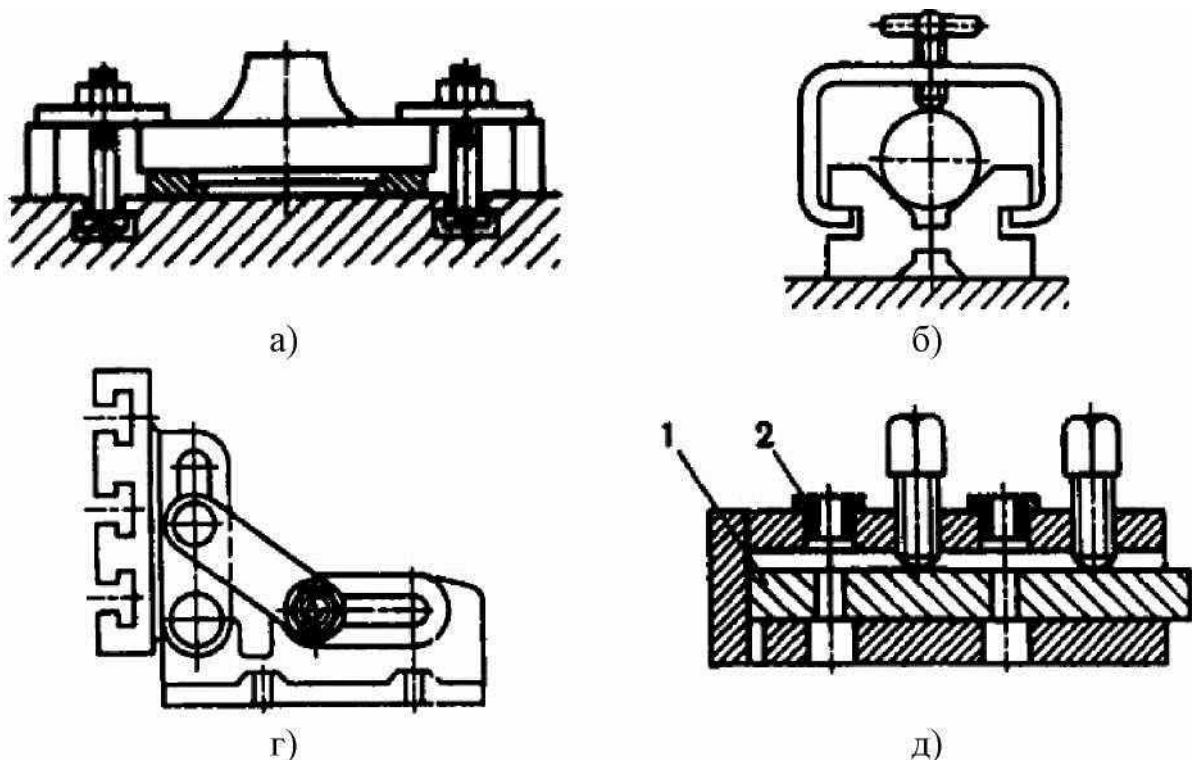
Пристосування для закріплення заготовок на свердлильних верстатах
